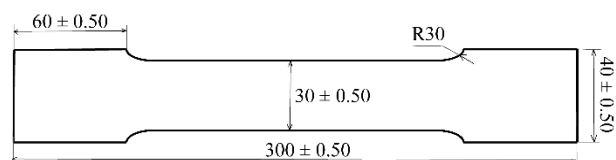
Эскиз (схема) алюминиевого образца.
